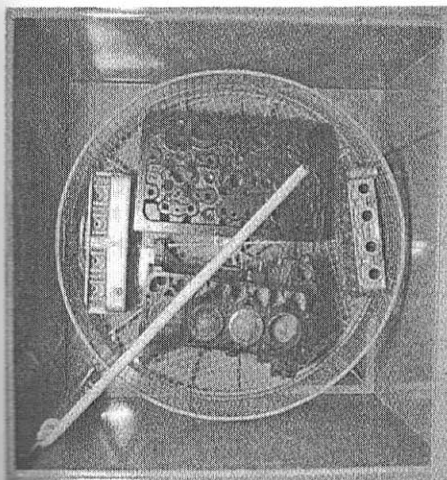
En el interior del tambor de la máquina lavadora rotativa se debe colocar el bloque, junto con la culata y todas aquellas piezas que se desee lavar y desincrustar.
